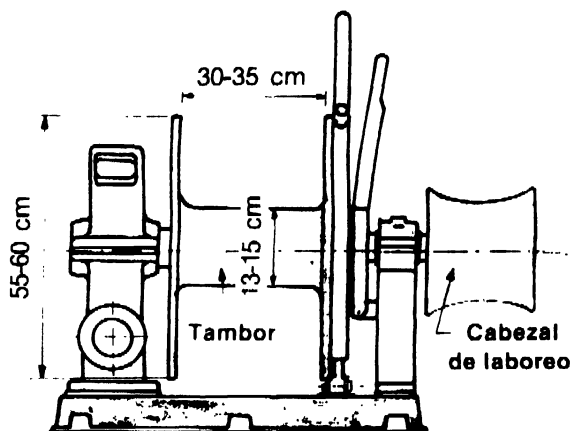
Maquinilla de un tambor y un cabezal de laboreo
